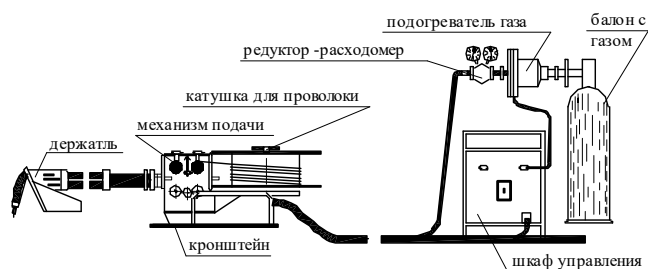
Схема сварки полуавтоматом в защитном газе
